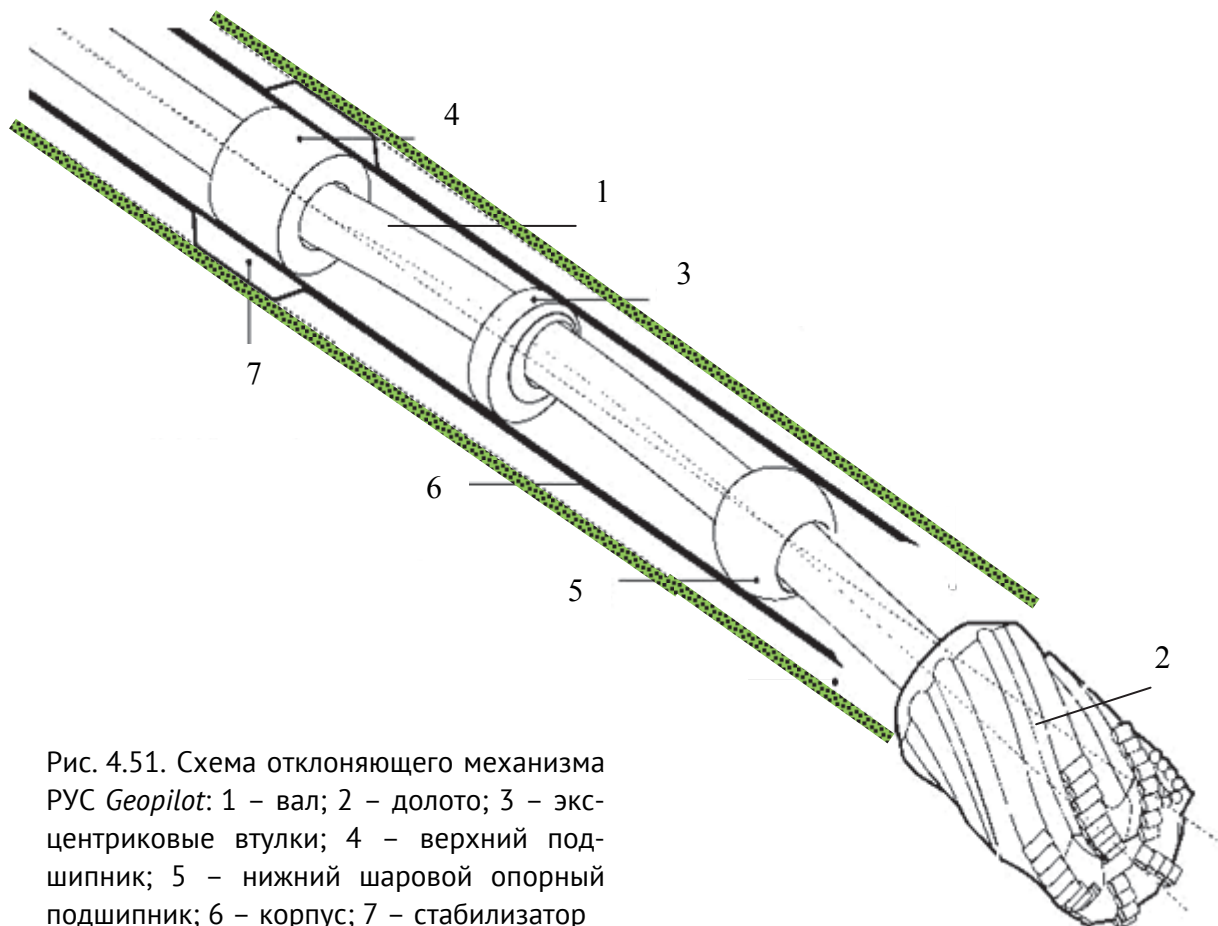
Схема отклоняющего механизма РУС *Geopilot*: 1 – вал; 2 – долото; 3 – эксцентриковые втулки; 4 – верхний подшипник; 5 – нижний шаровой опорный подшипник; 6 – корпус; 7 – стабилизатор
